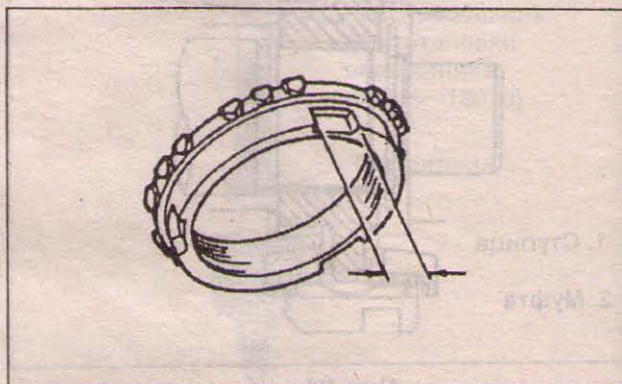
А—38 ПРОВЕРКА ШИРИНЫ ШПОНОЧНОГО ПАЗА
